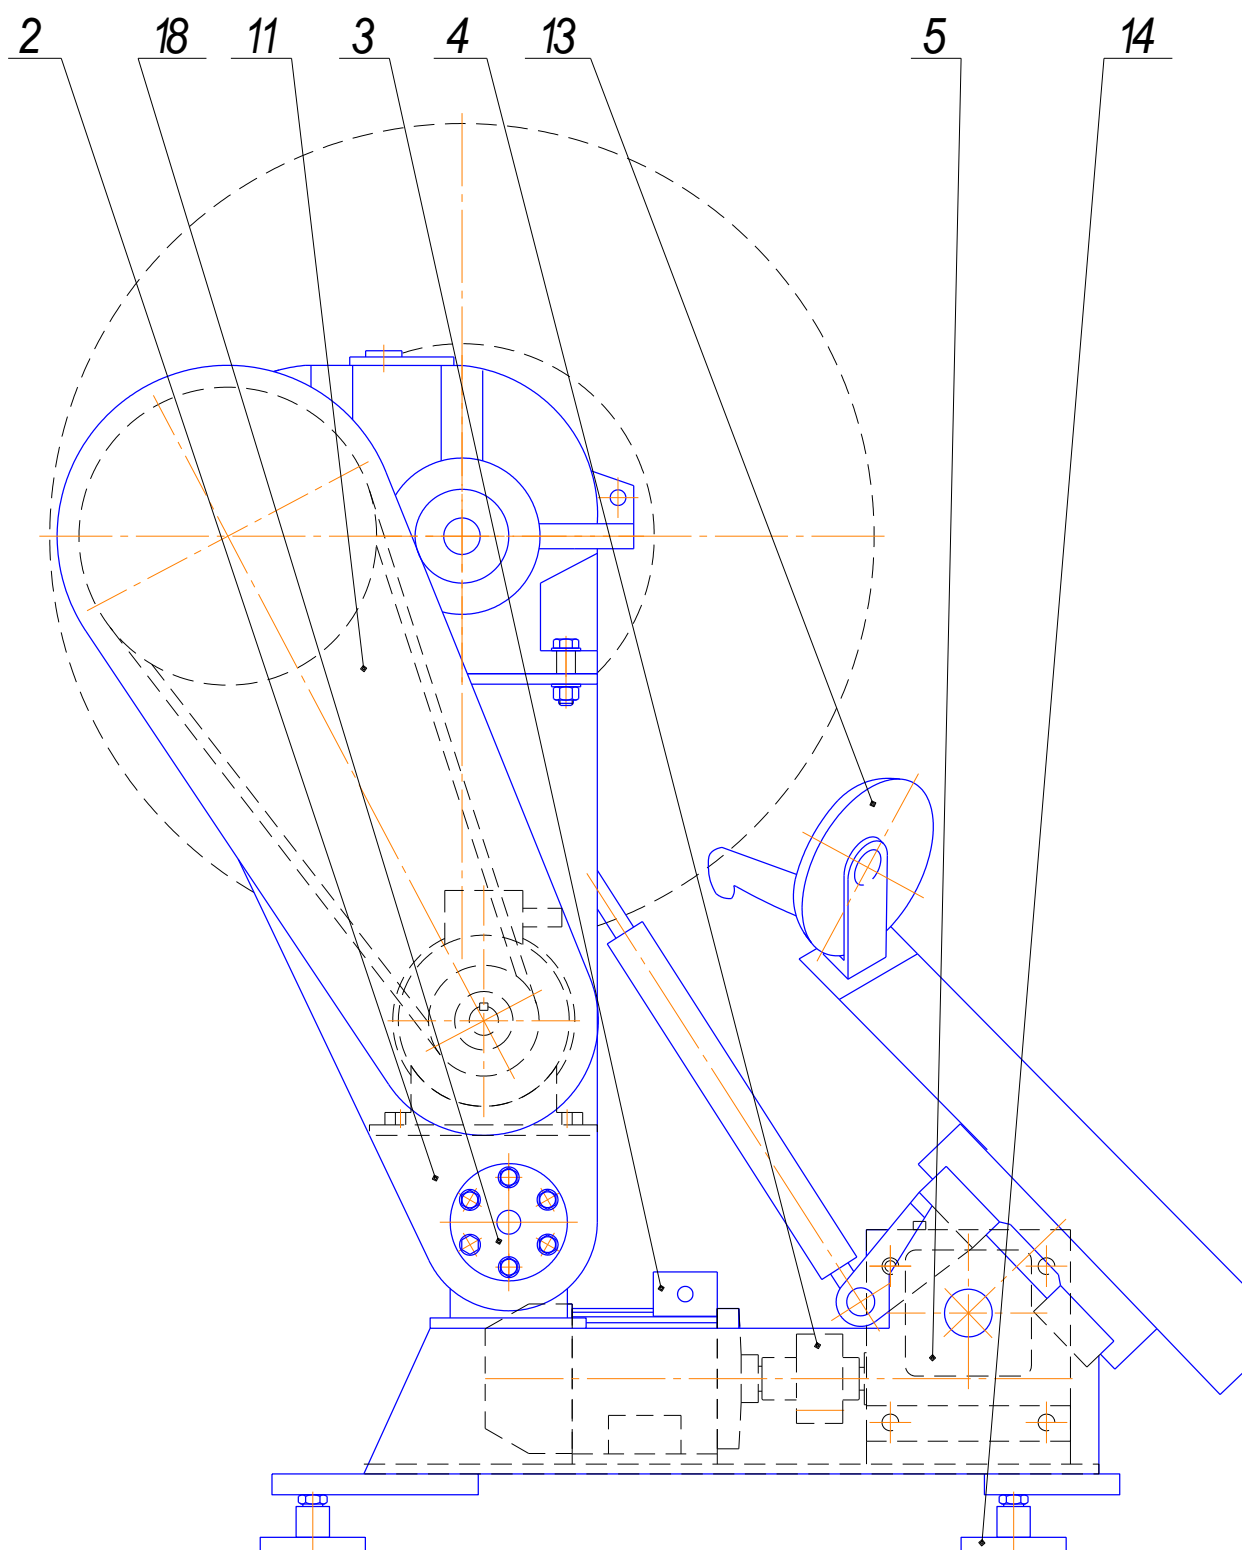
б - Схема шиномонтажного стенда для грузовых автомобилей
